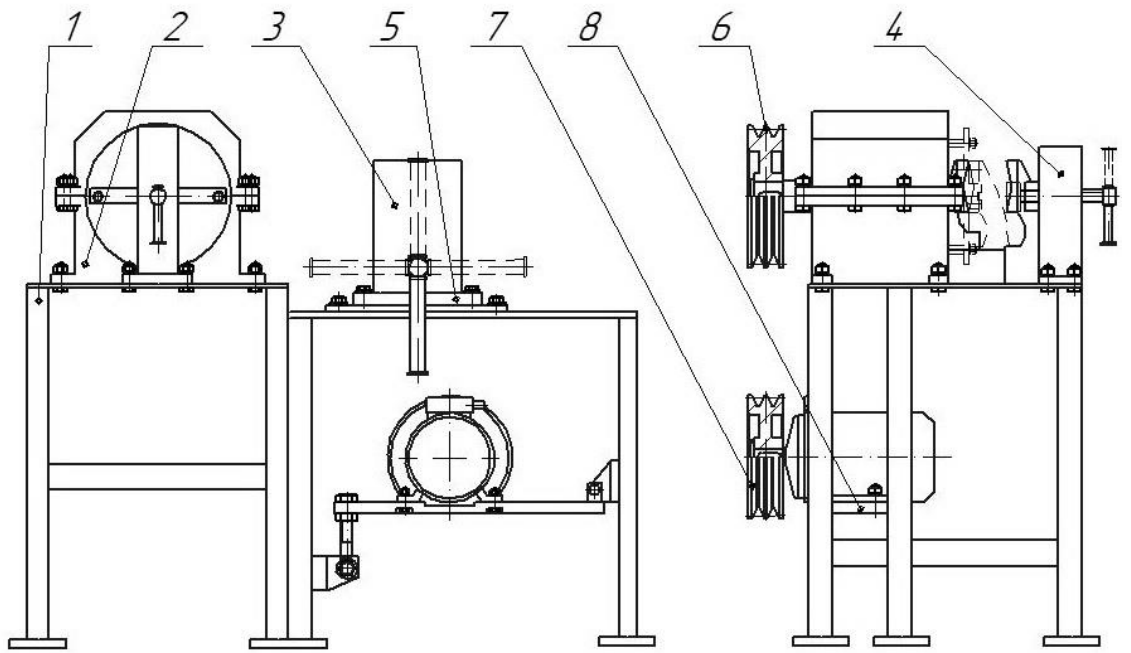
Стенд для випресовки підшипників хрестовин:
